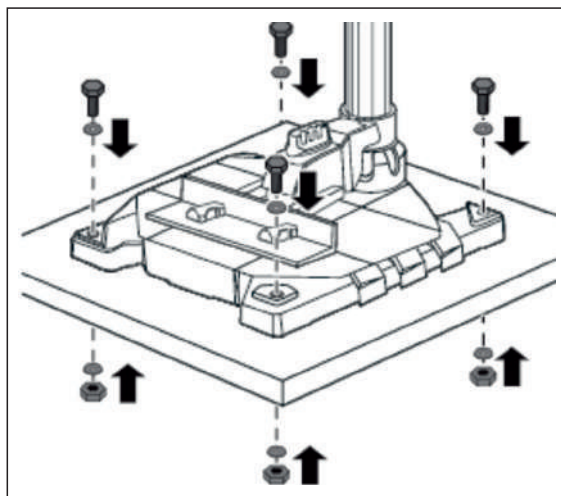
Крепление на верстаке/ Fig. 6 Bench Mounting
